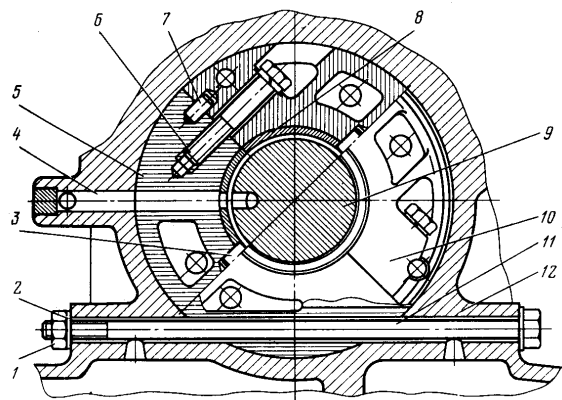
Опора среднего коренного подшипника (вид со стороны носка коленчатого вала):
